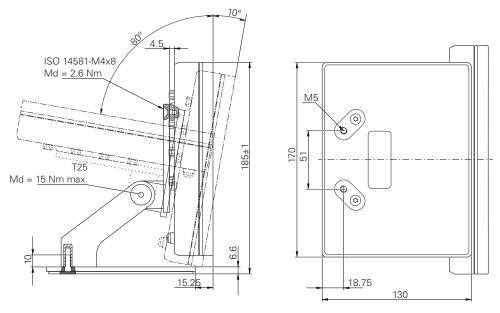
Dimensiones del aparato con pie de soporte Multi-Pos
